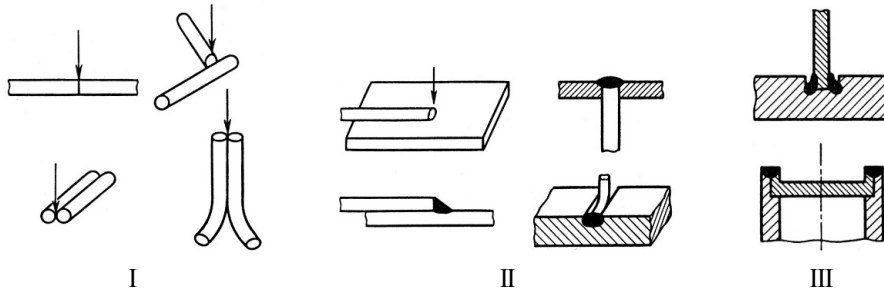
Деякі типи зварних з'єднань тонких металів:
